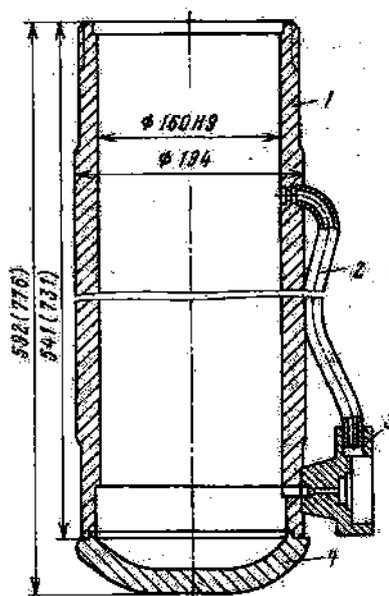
Цилиндр стойки крепи М87Д: 1 - труба; 2 - трубопровод; 3 - бобышка; 4 - дно
